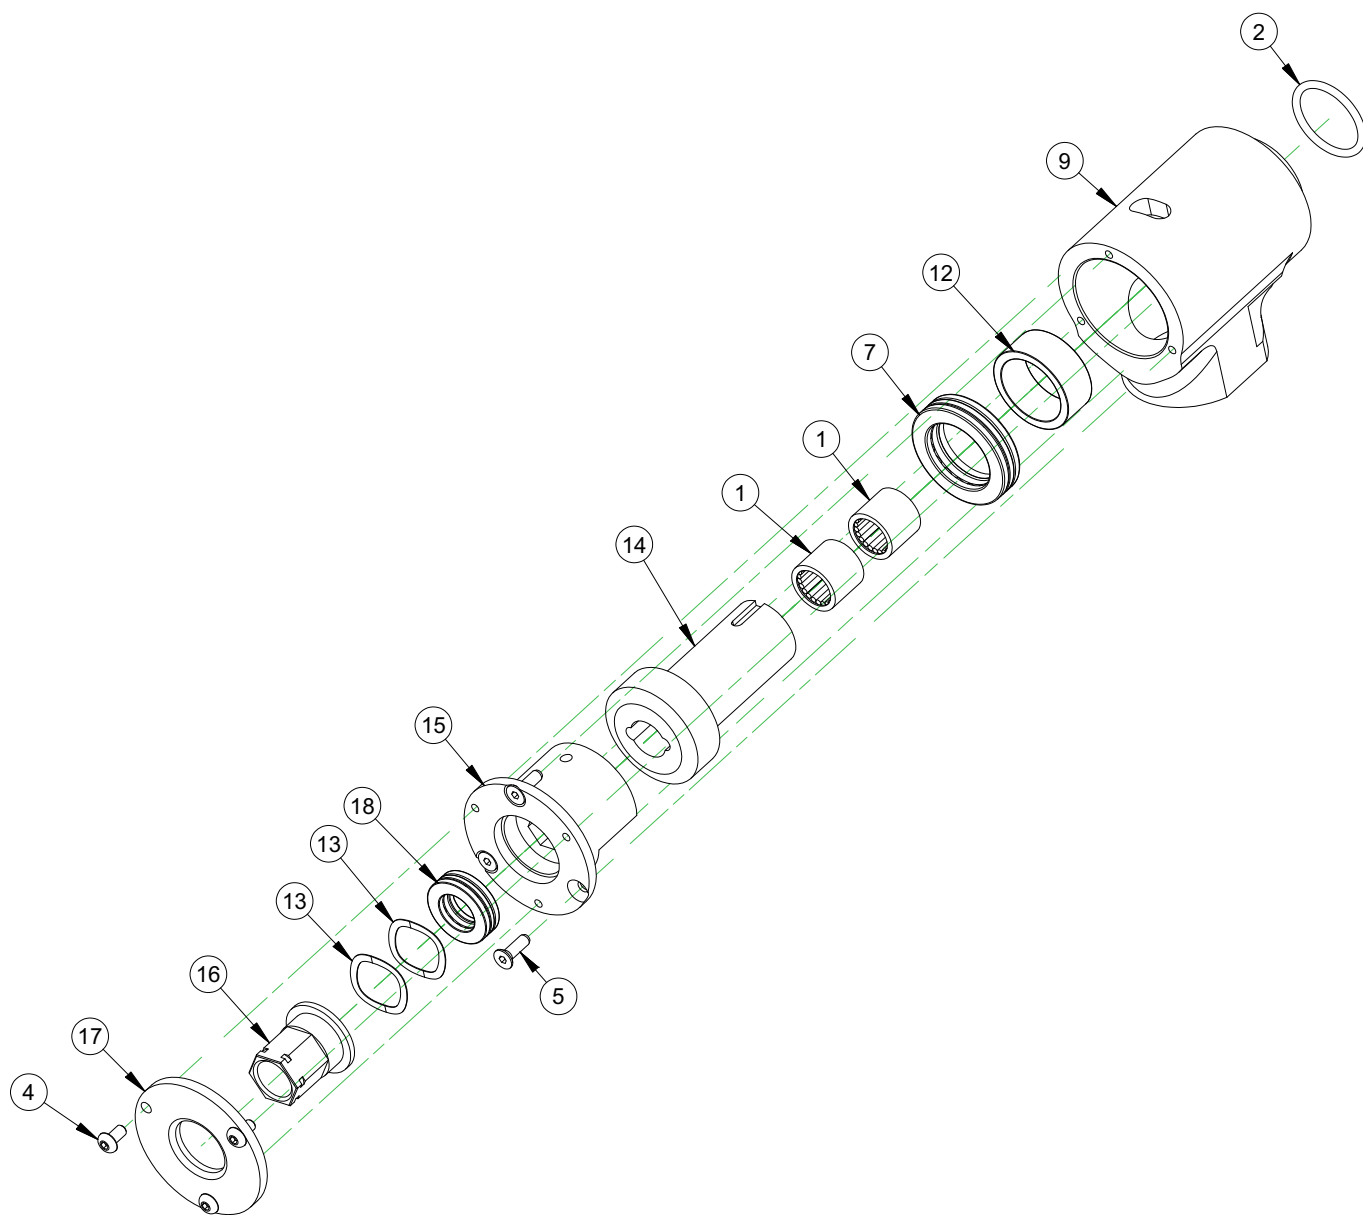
MONTAJE DE LA UNIDAD BASE 2 DE LA BF-R BOILER GUN (N/P 98894)
